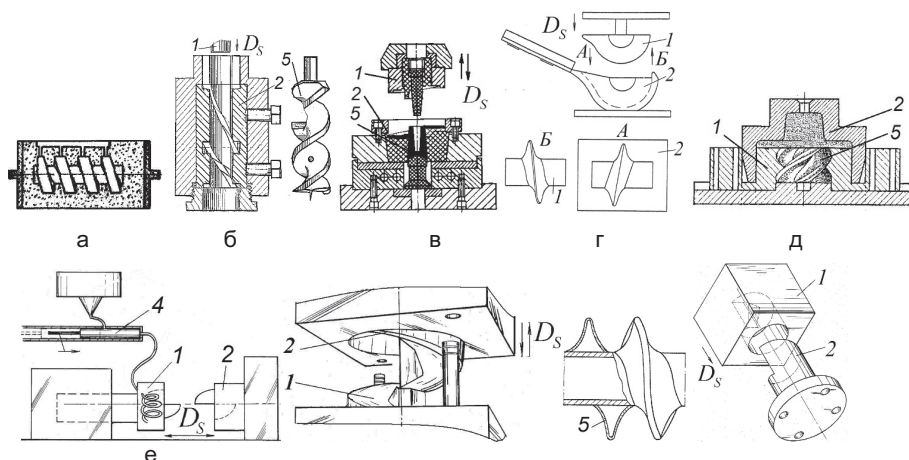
Фрагменты библиотеки типовых технологических схем формообразования литых ШЗ: а – одноразовая песчано-глинистая форма; б – жидкостная штамповка с выдавливанием жидкого металла; в, г - жидкостная штамповка с кристаллизацией под давлением; д – пресс-форма для литья по выплавляемым моделям; е - литье под давлением
